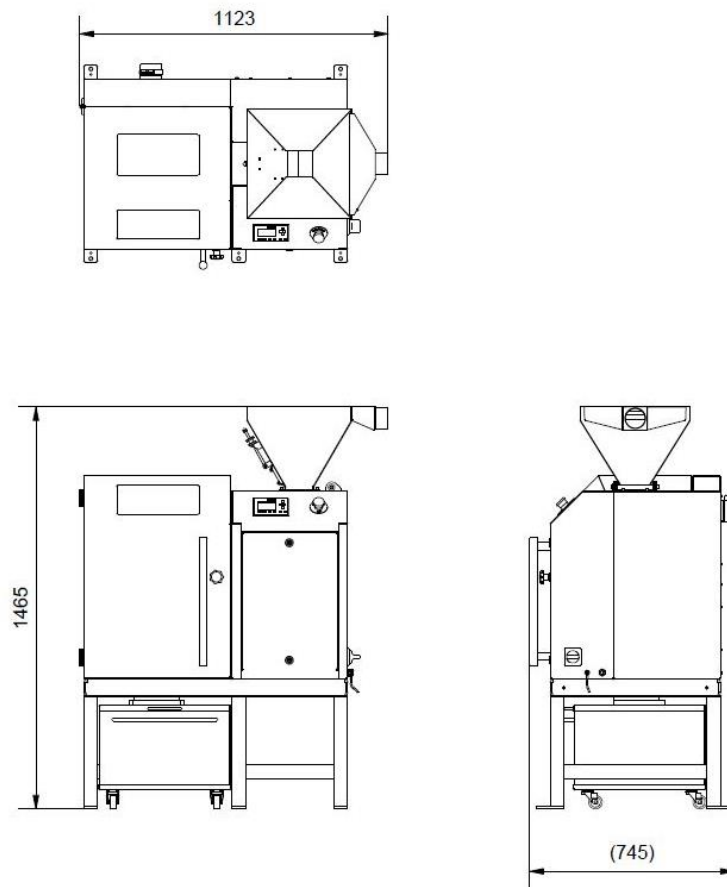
Дверца корпуса закрыта — воронка 30 л
